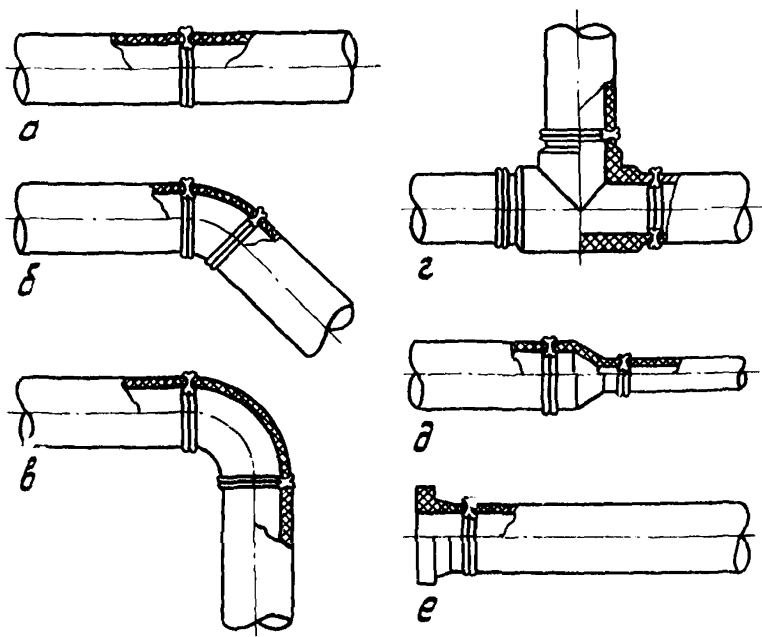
Сварные стыковые соединения труб и соединительных деталей из ПНД:
